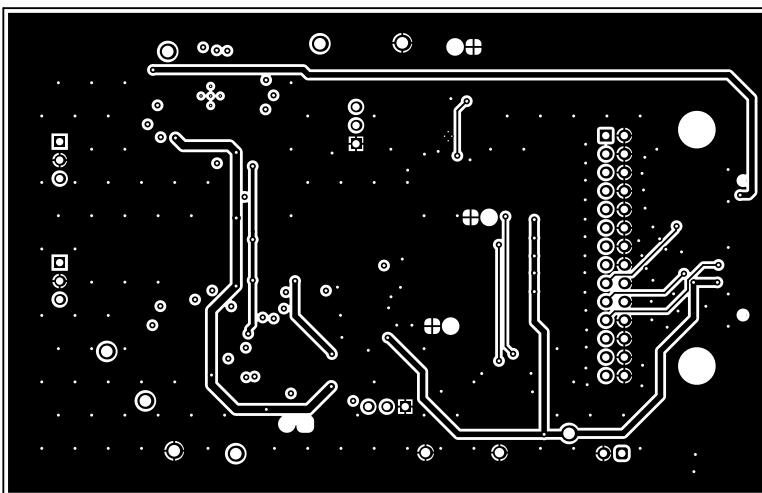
ADS1282EVM 的 PCB 布局 (底层)
